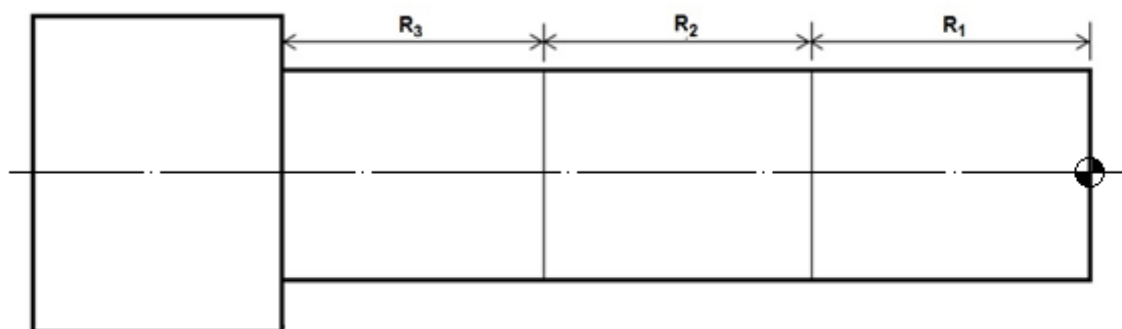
Corpo de prova após a uniformização da superfície de usinagem.
